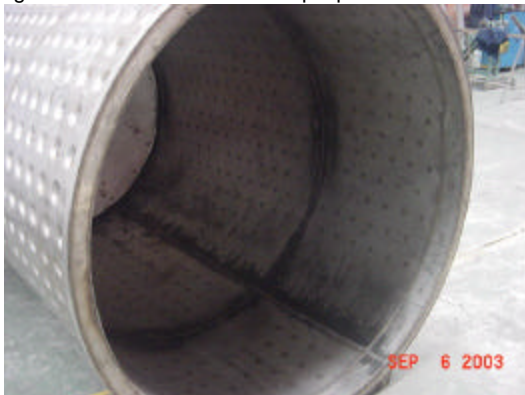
Soldadura TIG. Fabricación de chaqueta de vapor para tanque
